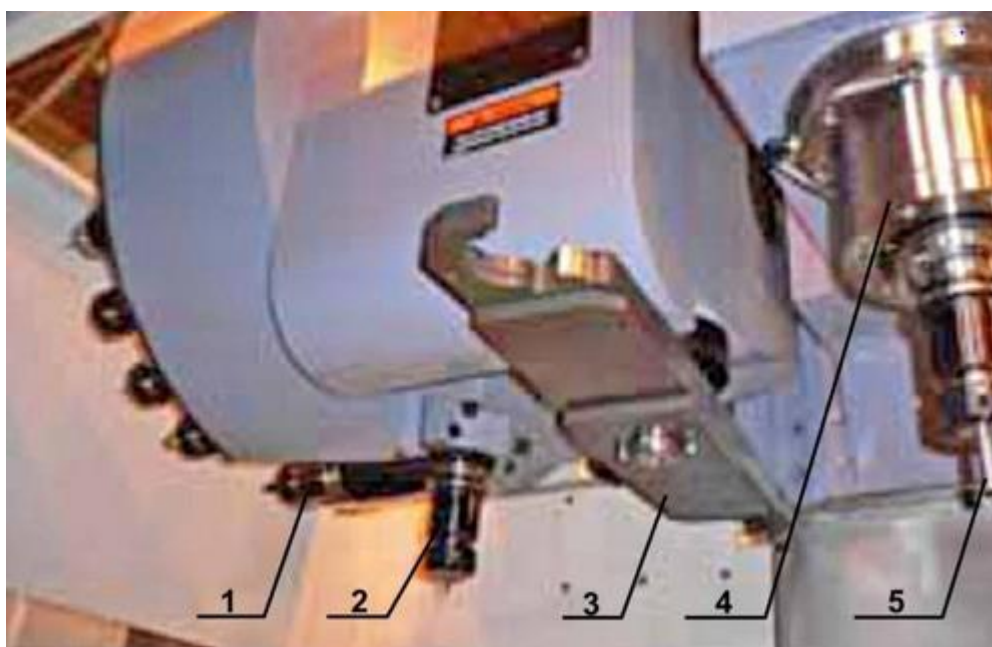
Процесс смены инструмента: 1 – инструмент в магазине в штатном положении; 2 – инструмент на подготовительной позиции; 3 – манипулятор в штатном положении; 4 – шпиндель; 5 – инструмент в шпинделе
